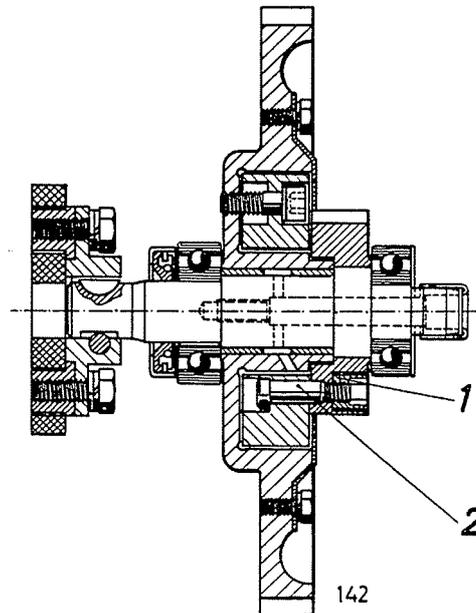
Einspritzpumpenantrieb F/A 6-12L 614 ohne Spritzversteller
